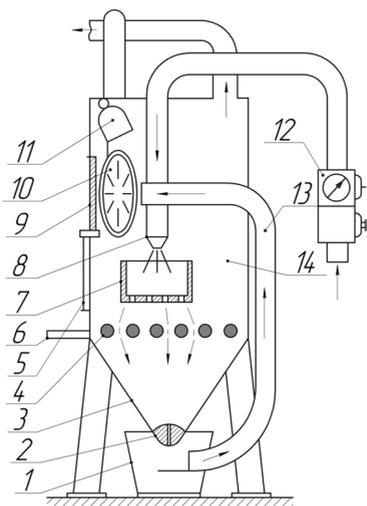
Схема обработки дробью на пневмодробеструйной установке:
